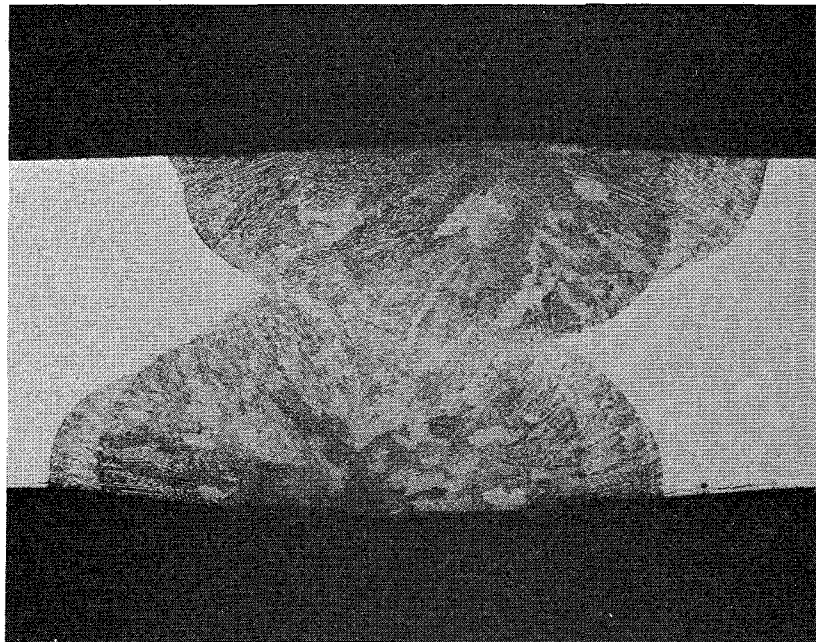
Makroaufnahme vom Querschliff der Schweißnaht bei Hastelloy C4 (Nr. 2.4610) im WS-Zustand nach vollständiger Entzunderung vor dem Schweißen (ungestörte Schweißnaht) $V = 10:1$
